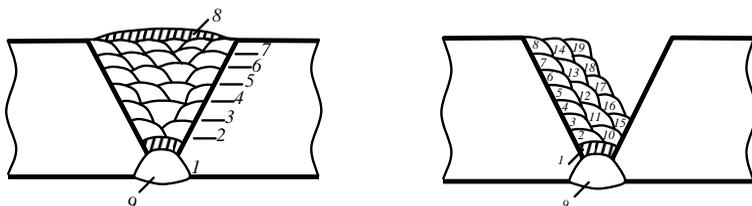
Рекомендуемая последовательность сварки стыка при односторонней разделке кромок
